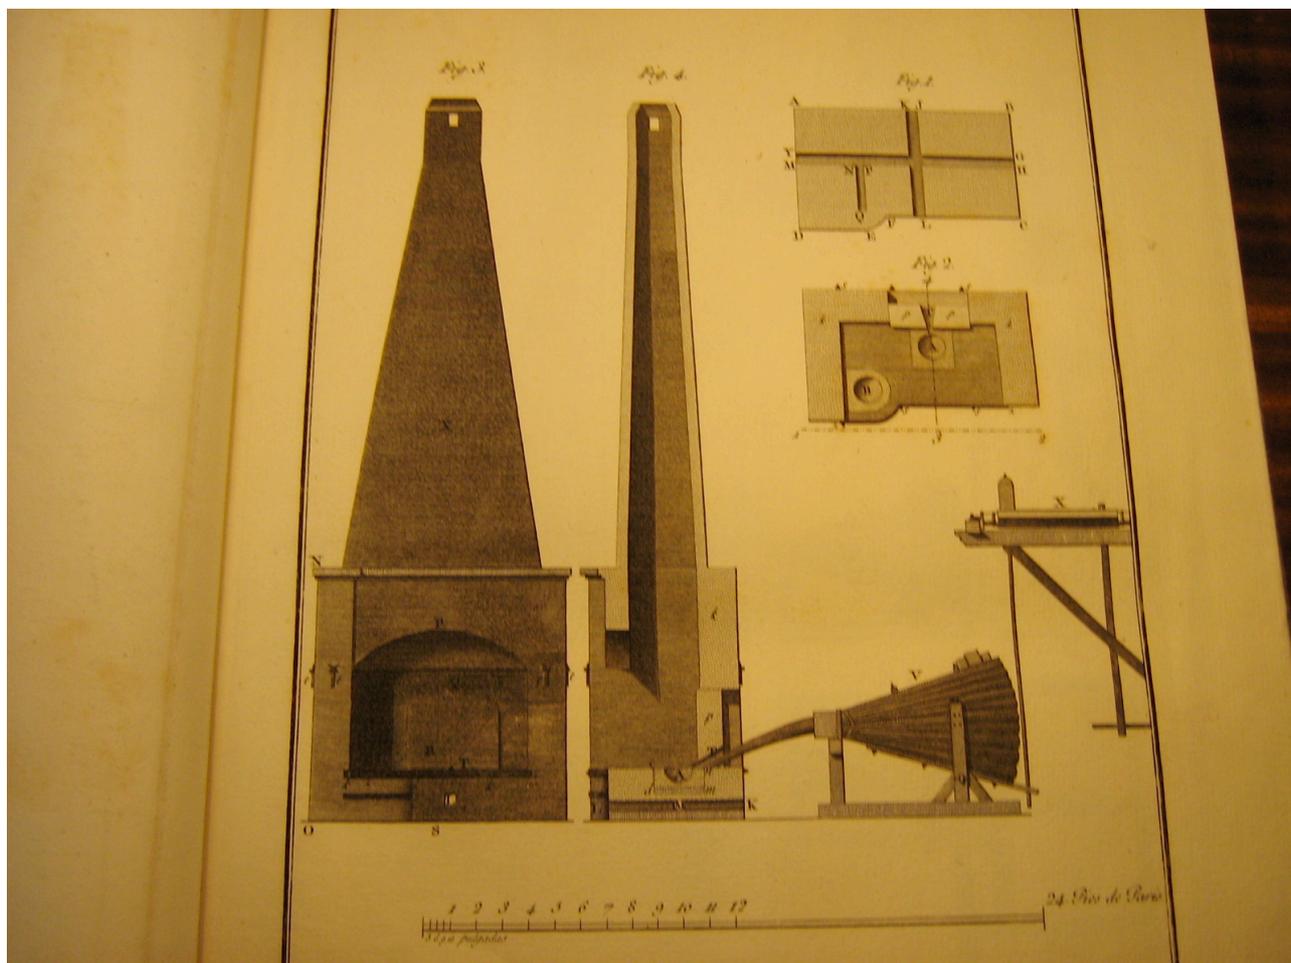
Planta y alzado de un horno de reverbero para afinar metales. *Láminas del Tratado de Artillería* de Tomás de Morla, 1783.
